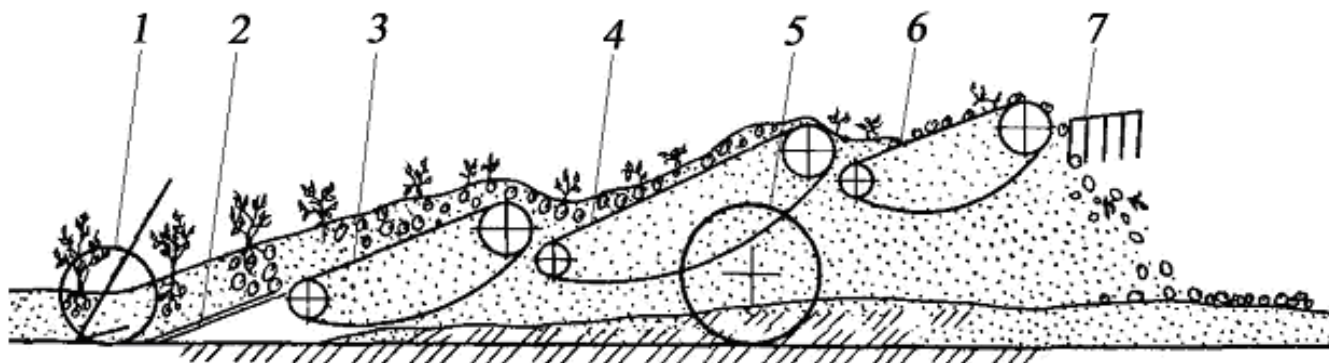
Функціональна схема швидкісного картоплекопача КСТ-1,4: 1 - копіювальне колесо; 2 - леміш; 3 - швидкісний елеватор; 4 - основний елеватор; 5 - ходове колесо; 6 - каскадний елеватор; 7 - гребінки
